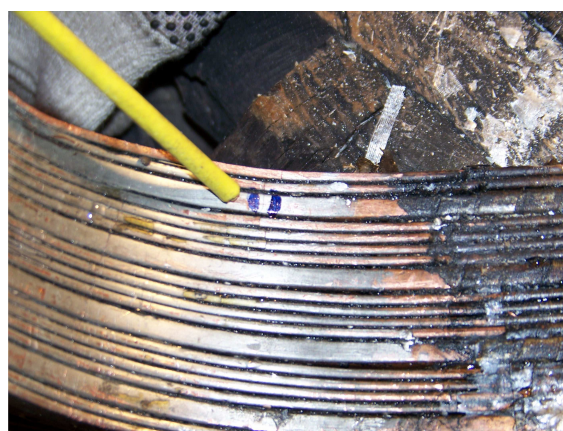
Miejsce pęknięcia przewodu drażonego w strefie połączenia elektrycznego prętów GW z DW
